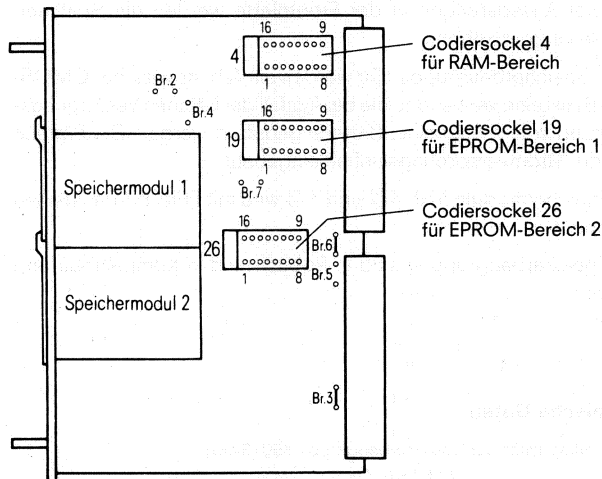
Einbau der Brücken und Codiersocket (Lieferzustand)
